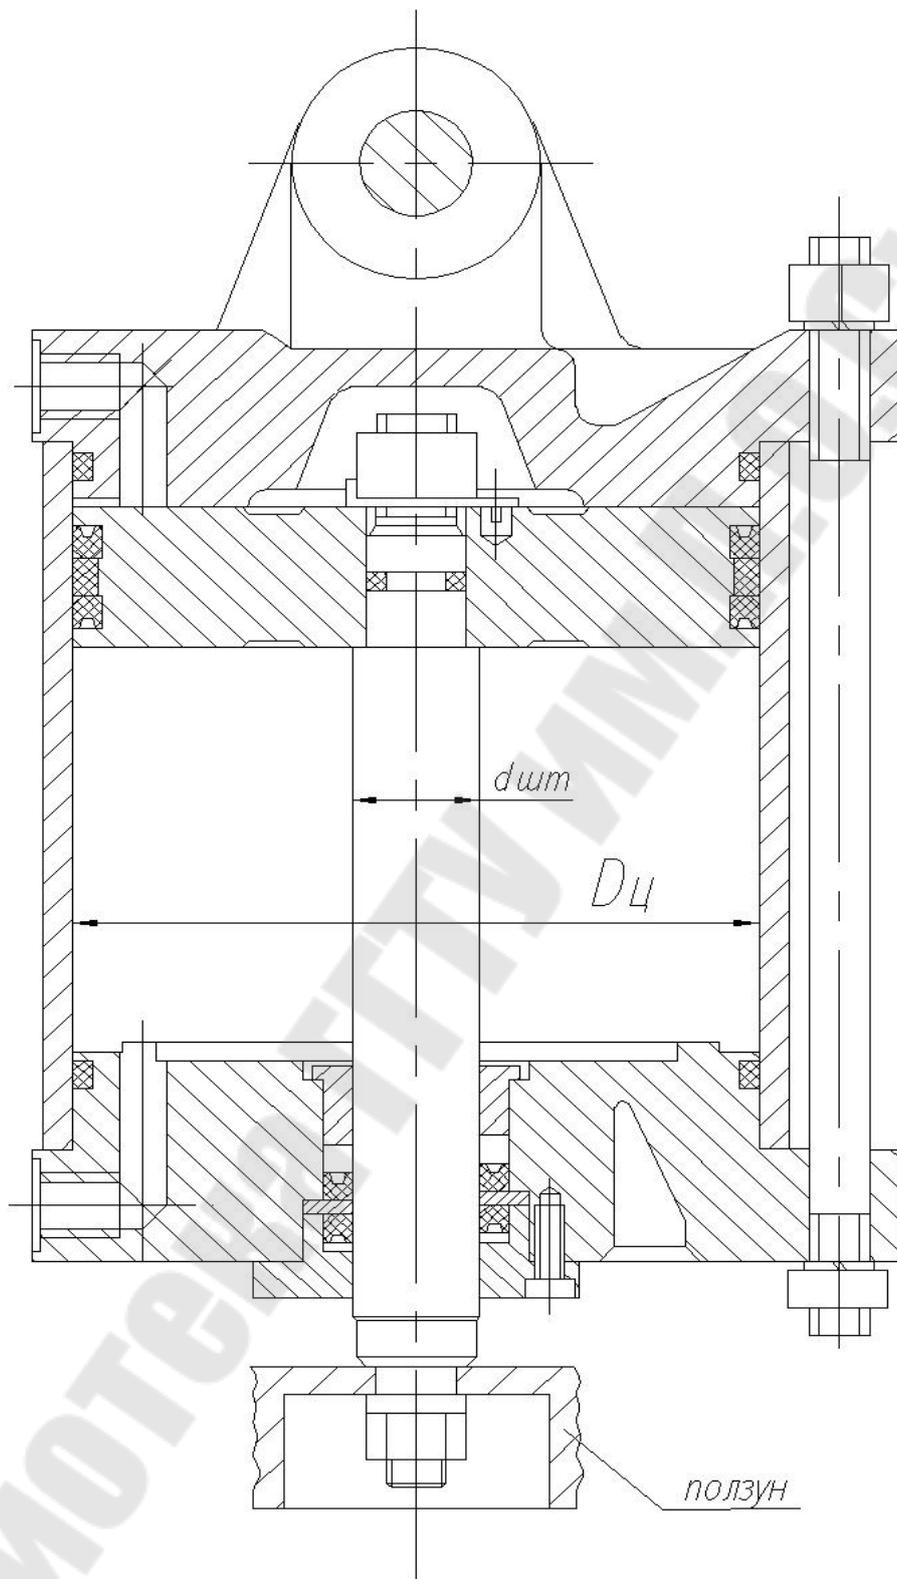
Установка пневматического уравновешивателя на проушине
